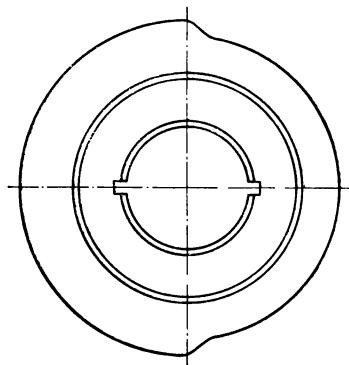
Профиль кулачка к затыловочному устройству резьбошлифовального станка
